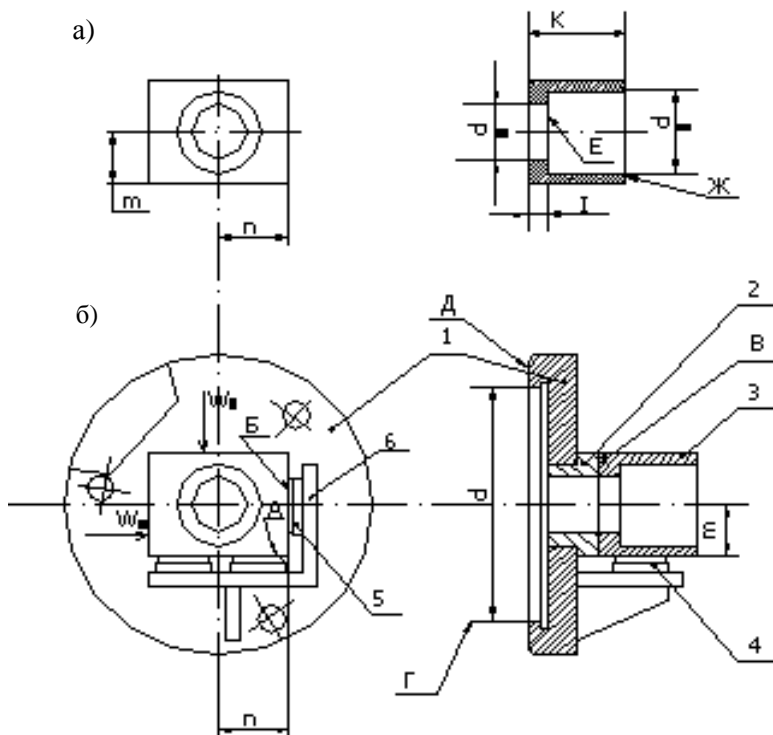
Схема установки заготовки (а) в приспособлении (б) на токарном станке
